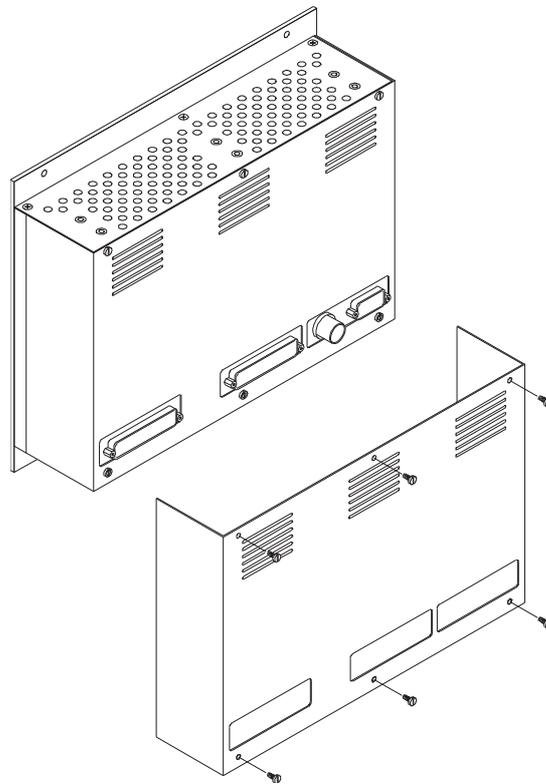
Entfernen des Abdeckblechs auf der Rückseite
